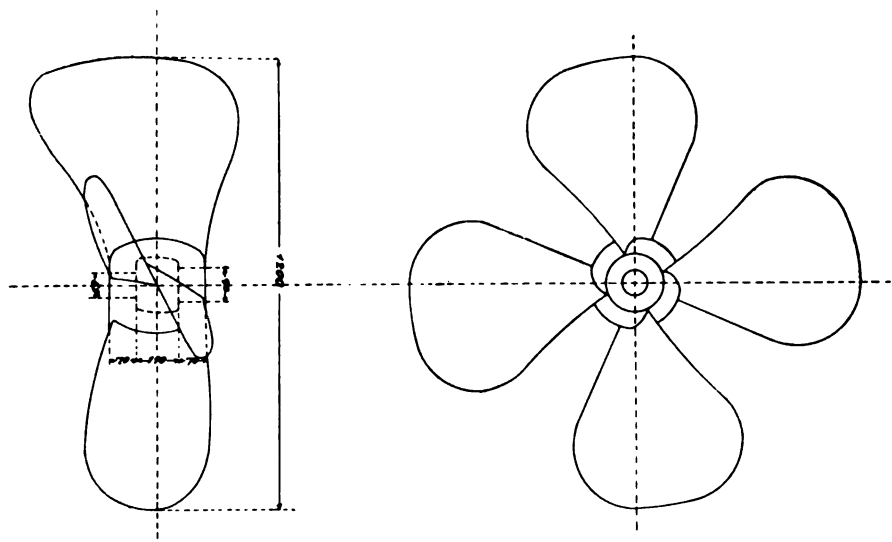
Langflüglige Schraube für einen 100 PS starken Schleppdampfer. 1:20.
